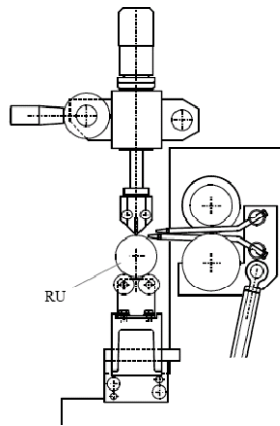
Esquema de las barras soldadoras.
